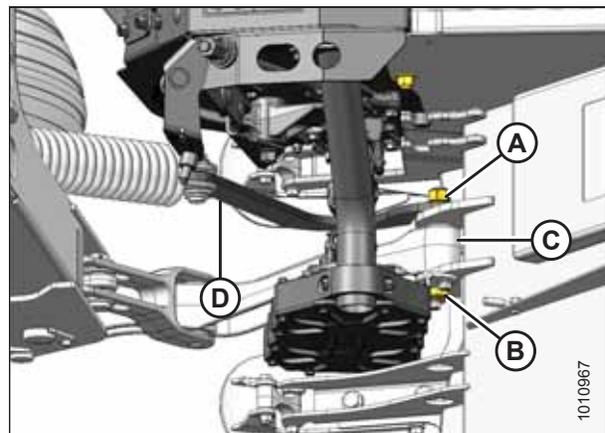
Côté droit du châssis porteur – Vue de dessus
